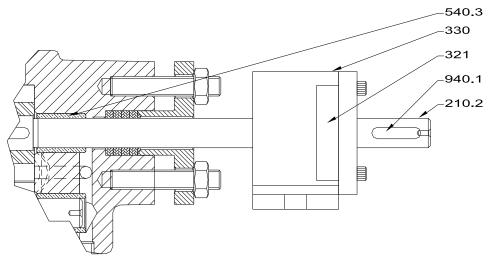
Desenho em Corte bomba FBE c/ Mancal Externo
